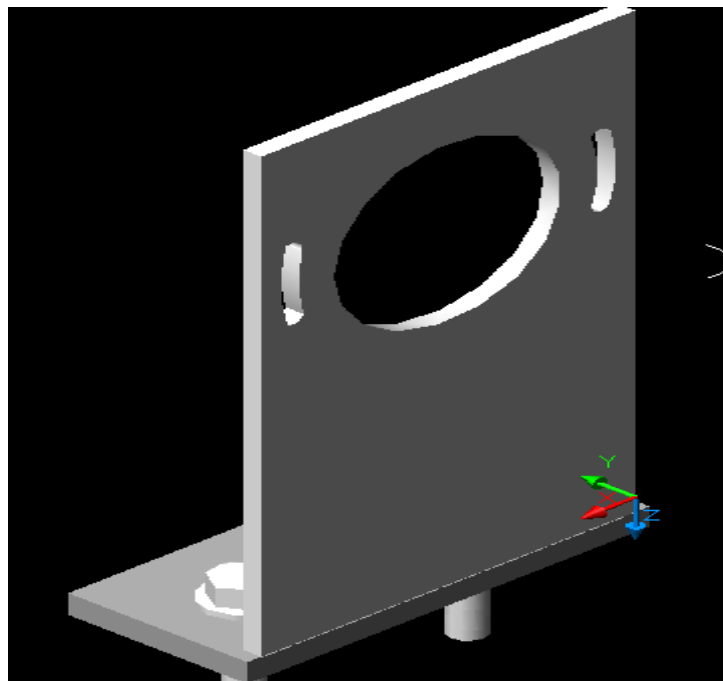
Vista isométrica 1 de la placa que soporta el motor de arranque
